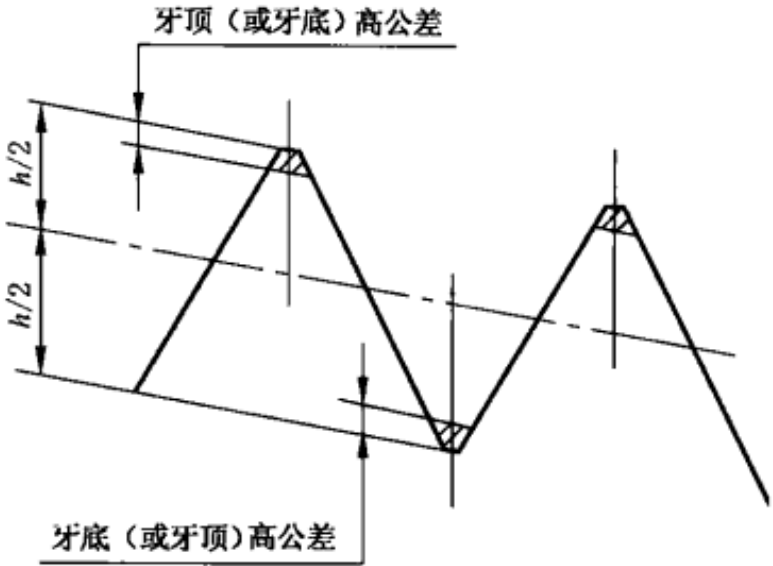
美制一般密封管螺纹的牙顶高和牙底高公差带位置
